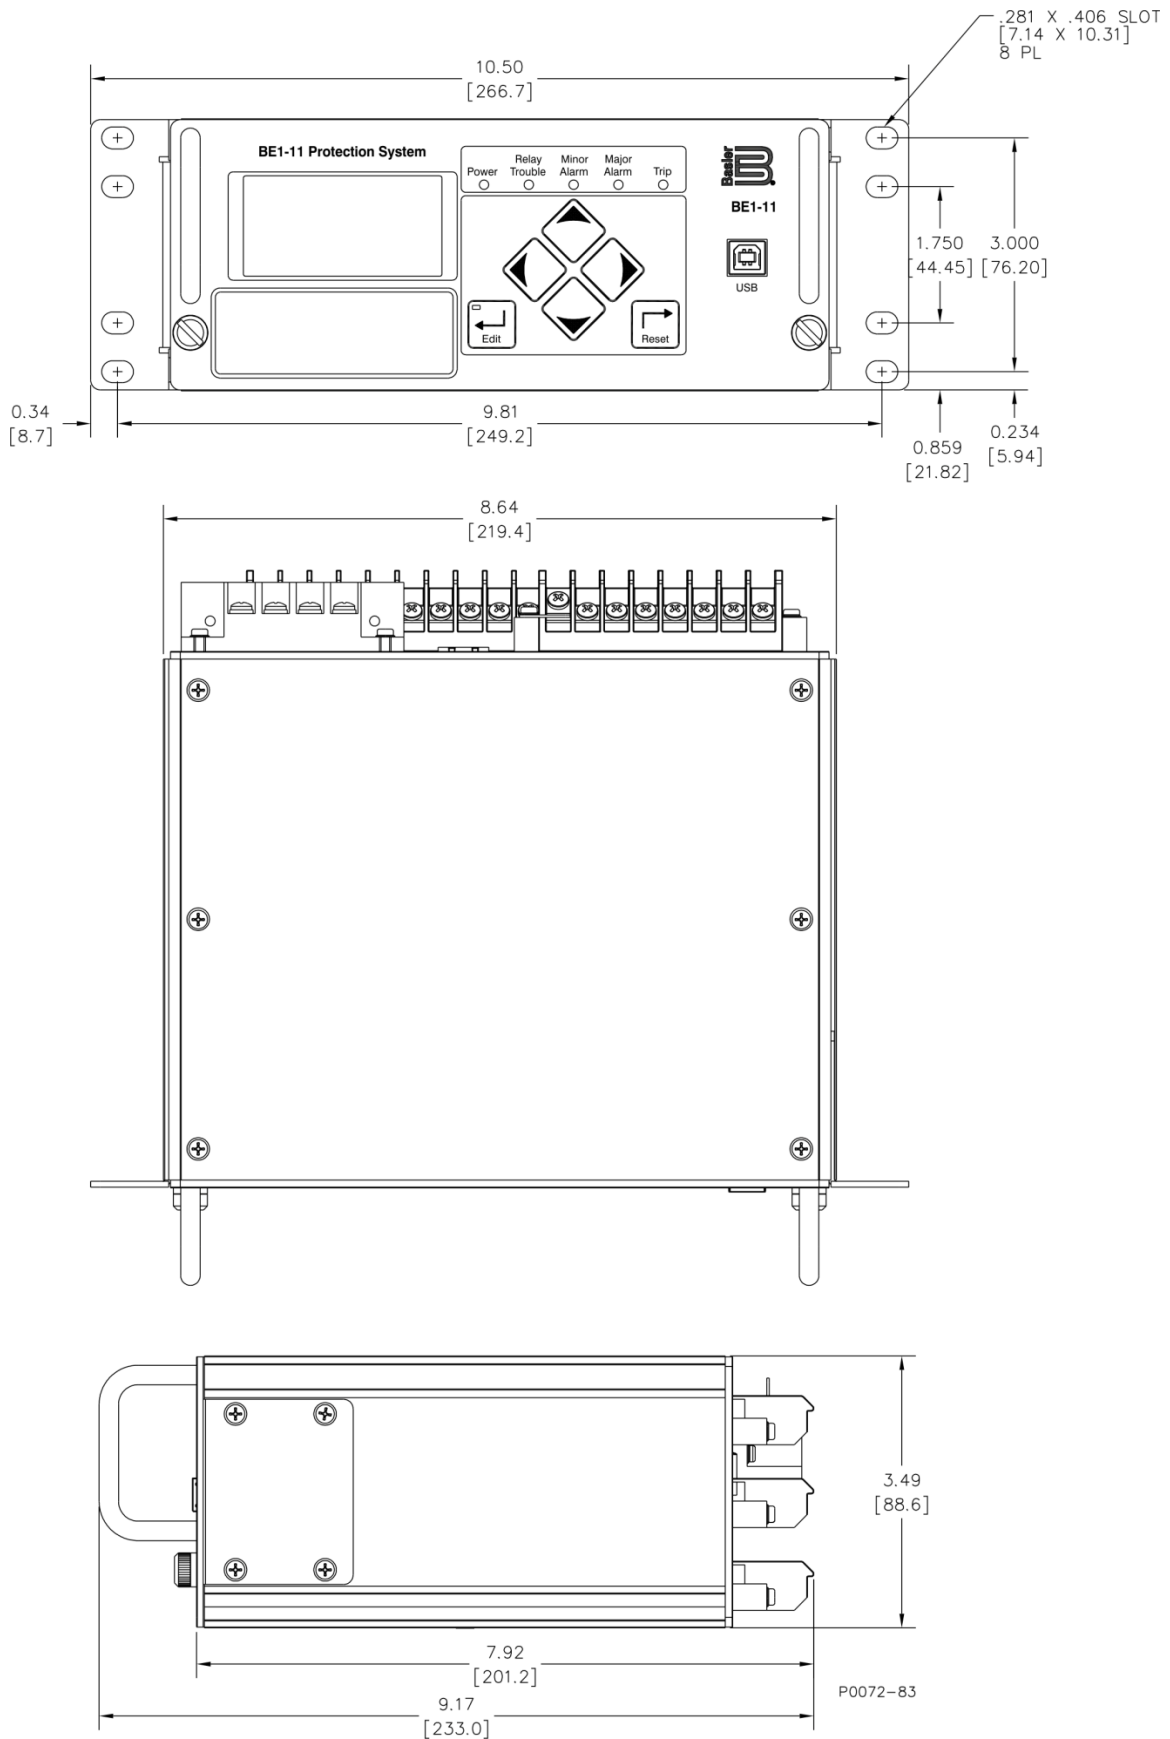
Dimensions du boîtier pour montage en tiroir H1
